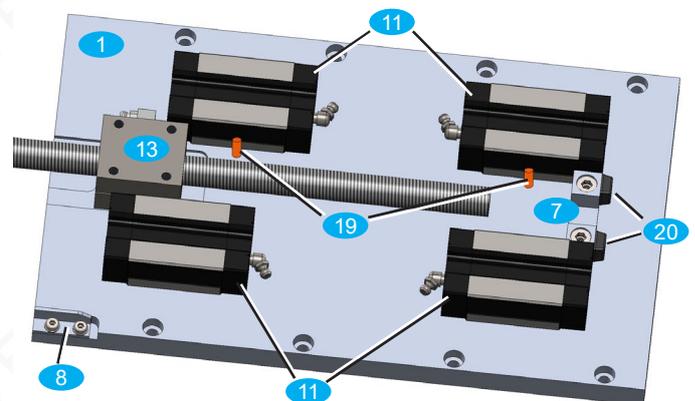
Montage von Führungswagen und Kugelumlaufmutter
